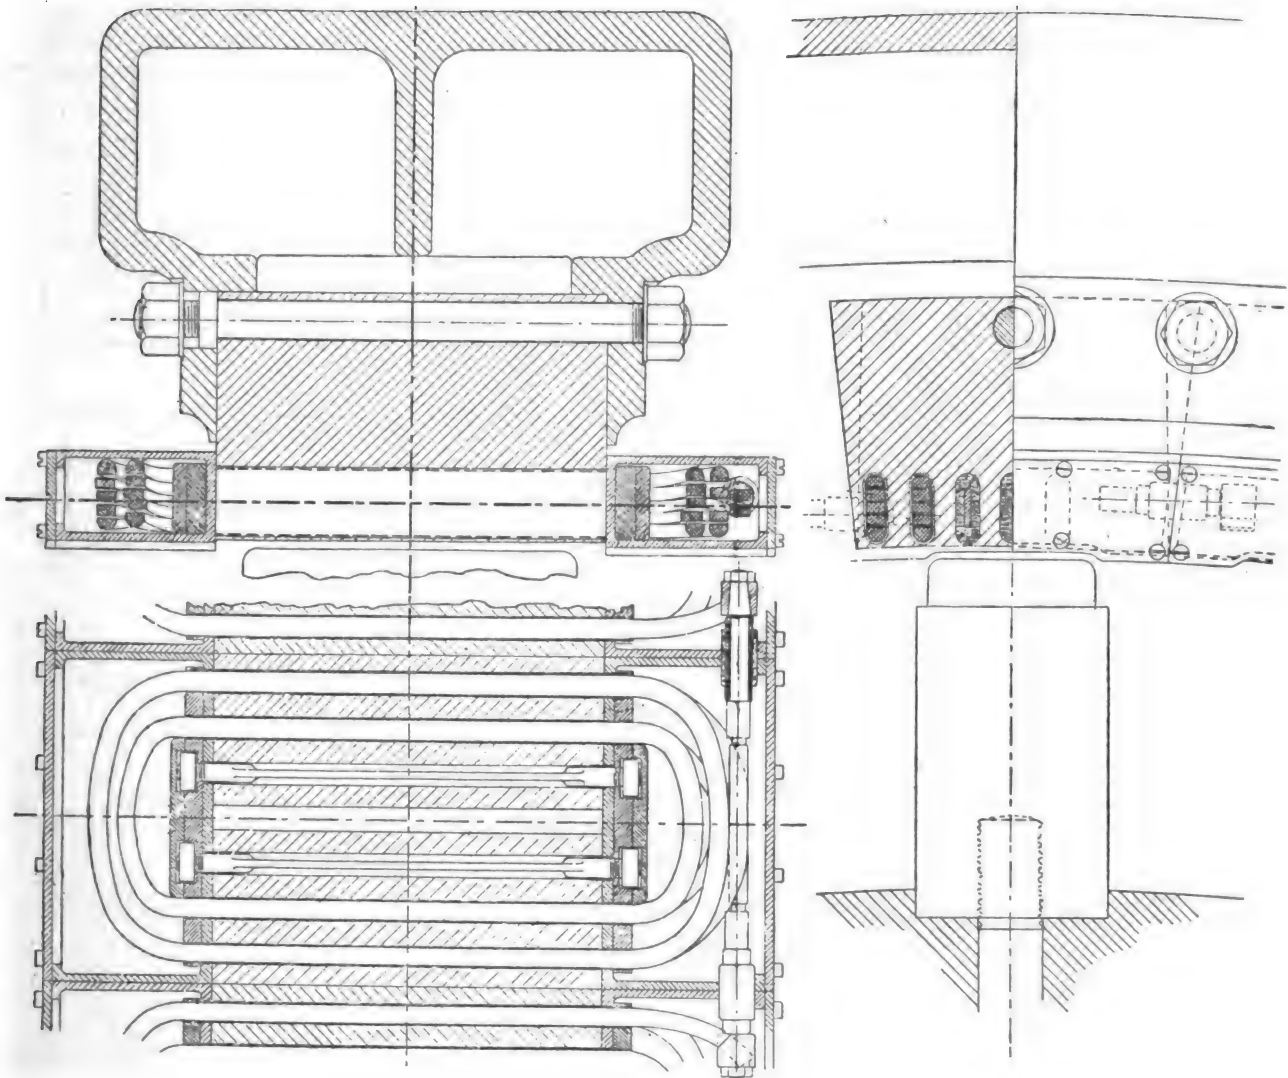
, 2 et 3. — Machines de Ferranti (1894). Coupe longitudinale, plan et coupe transversale.
